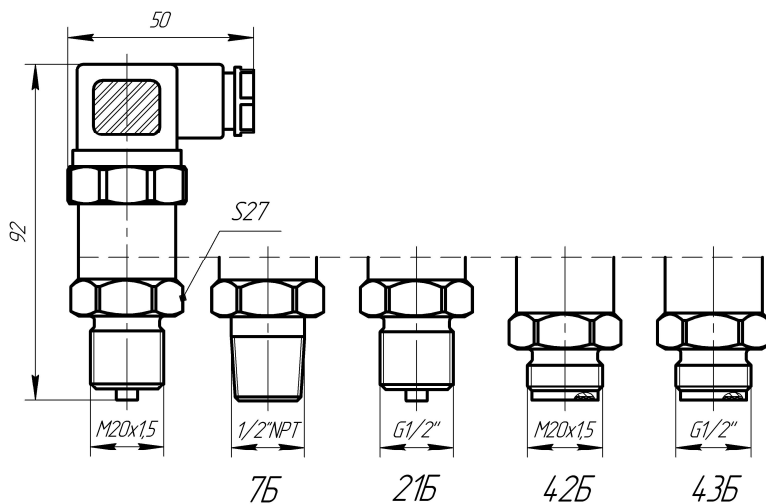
Габаритно-присоединительные размеры и внешний вид штуцерного преобразователя
